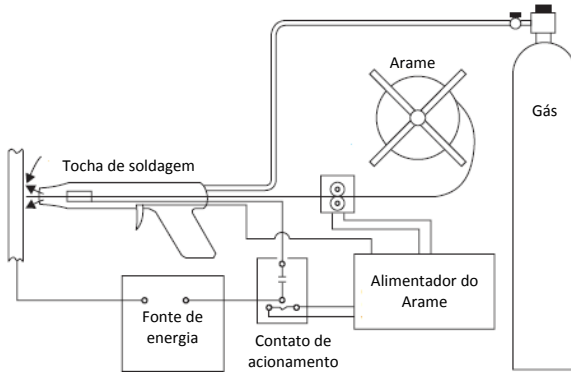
Processo básico de soldagem *Mig/Mag*.
